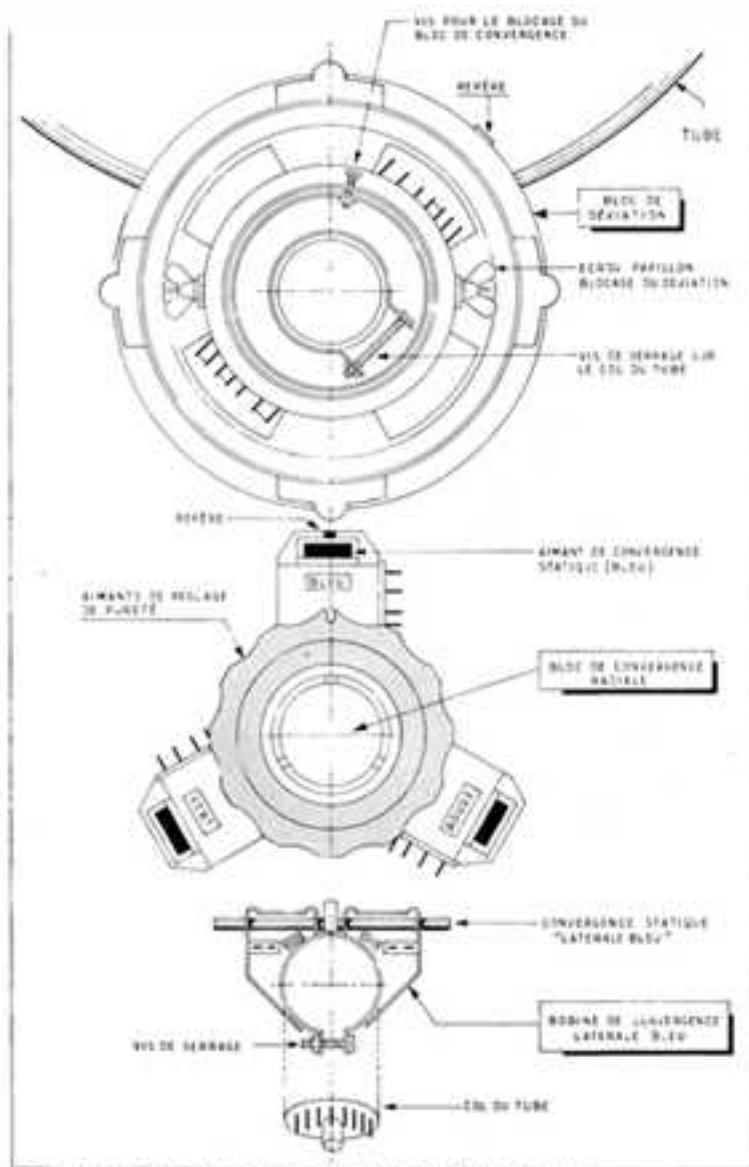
DISPOSITION DES ÉLÉMENTS AUTOUR DU COL DU TUBE ET ARRIÈRE DES RÉGLAGES.
